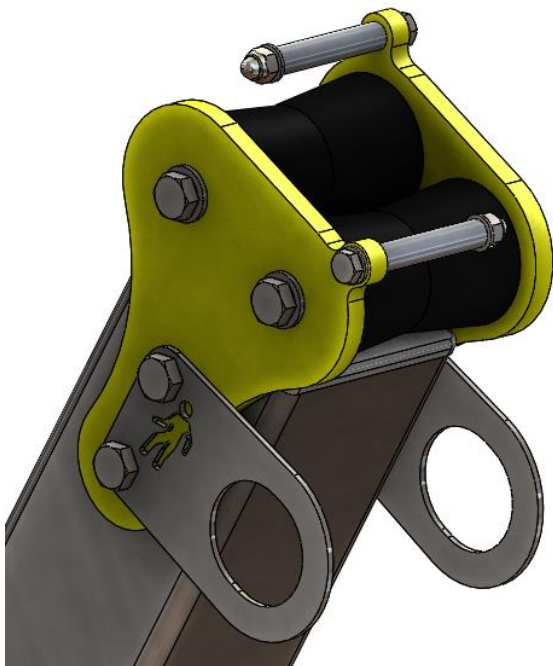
Conduzione della fune di lavoro del dispositivo fissato sul braccio mediante la puleggia.
